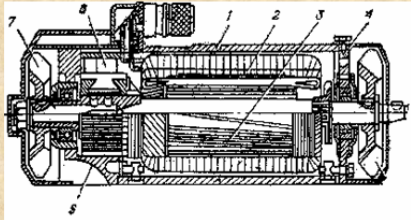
1-корпус; 2-обмотка возбуждения; 3- якорь;
